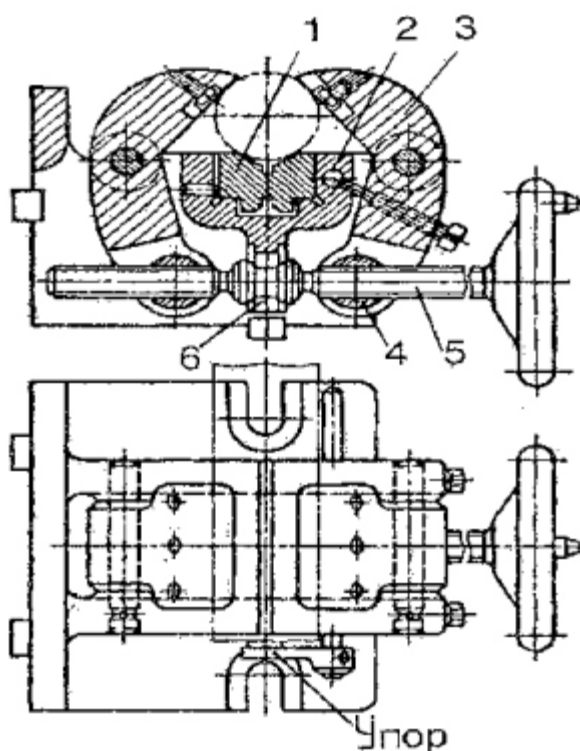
Конструкция самоцентрирующих тисков: 1 – сменная призма; 2 – корпус; 3 – рычаги; 4 – плавающие гайки; 5 – винт; 6 – подшипник.
